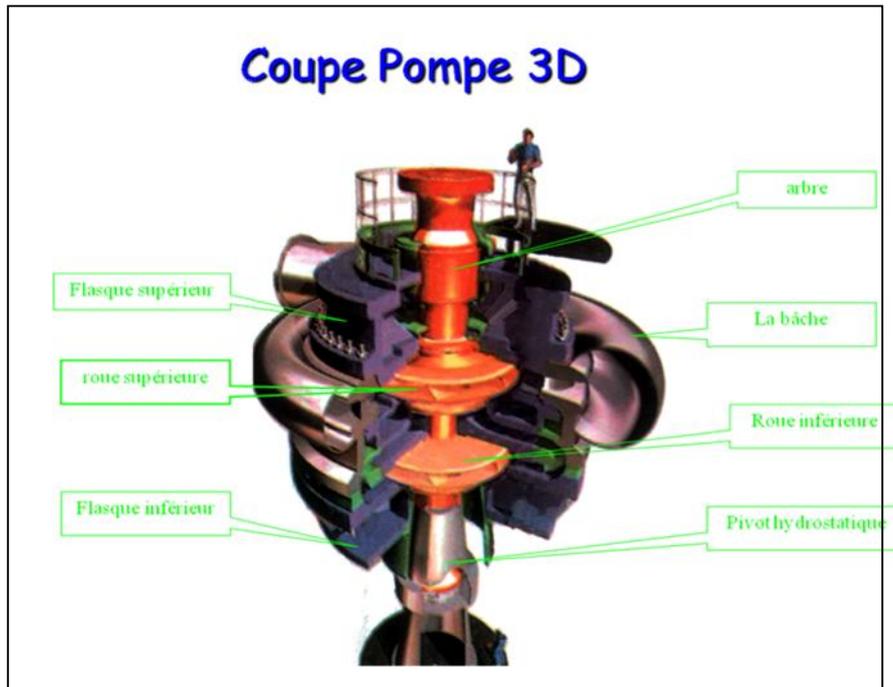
Coupe longitudinale de l'installation des pompes sur la tour
